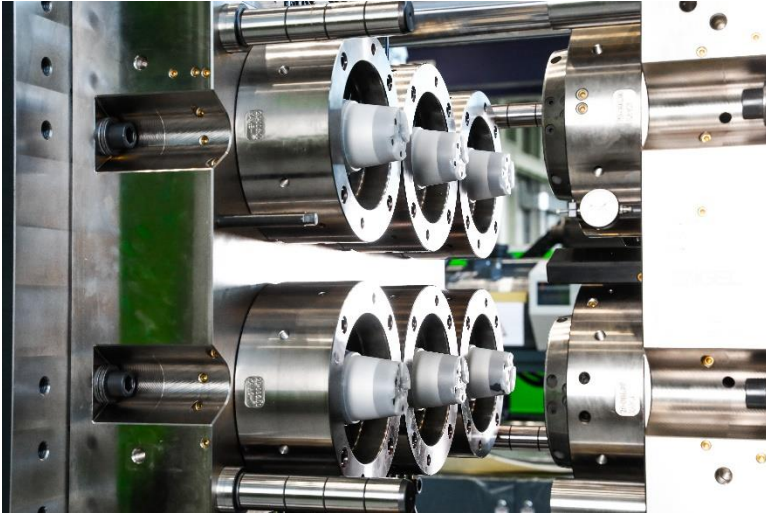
Glaroform 6-fach Pflanztopf Werkzeug auf einer vollelektrischen e-motion 765/280 T.
